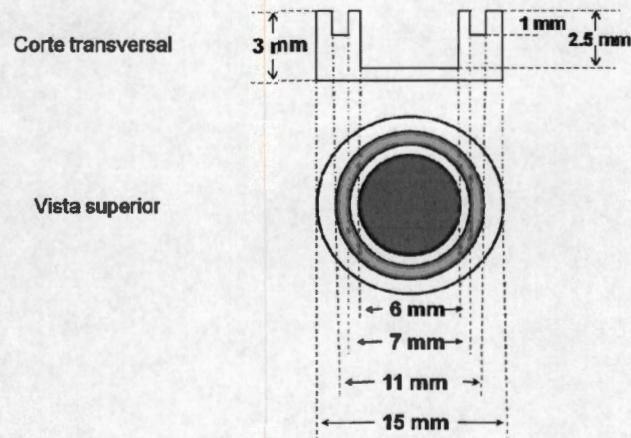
Esquema de dimensiones de la base de la celda de fluido. Se observa una vista superior y un corte transversal.
